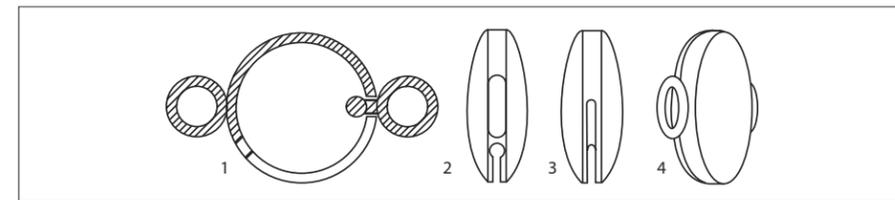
Линзовый замок: 1 — вид в разрезе; 2 — вид сбоку с соединительным ушком; 3 — вид сбоку с противоположной стороны; 4 — общий вид замка
